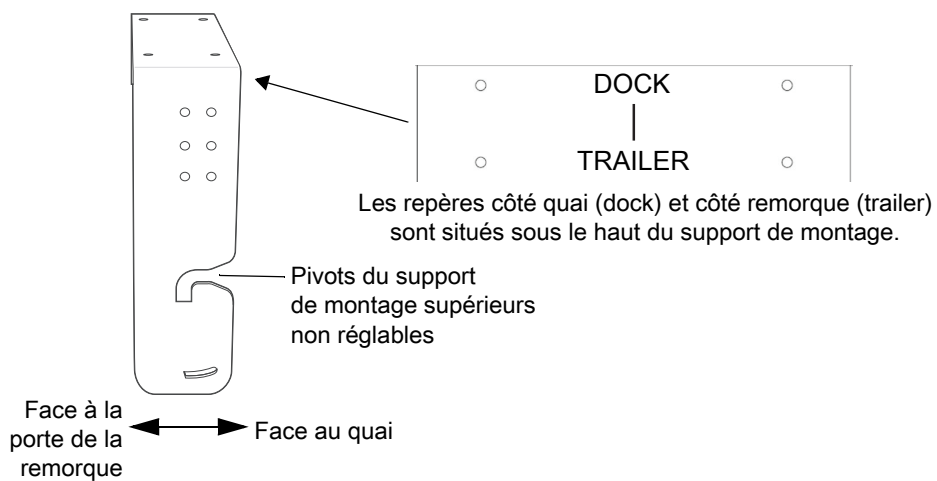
AS-000341-01 auquel le BI-000237-01-TLA est assemblé
